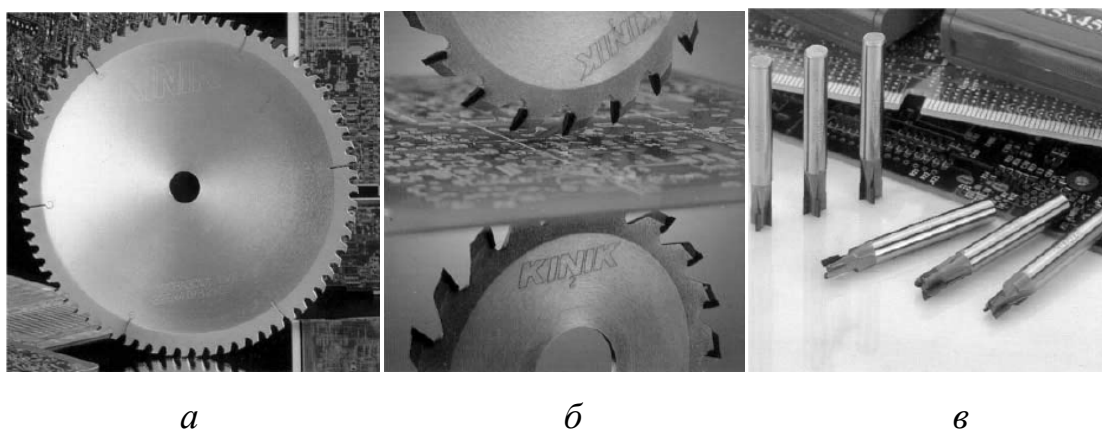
Приклад інструментів, що використовують PCD-алмаз (дискова пила (*a*); V-подібний різець (*б*); свердла / фрези (*в*)) [6]
